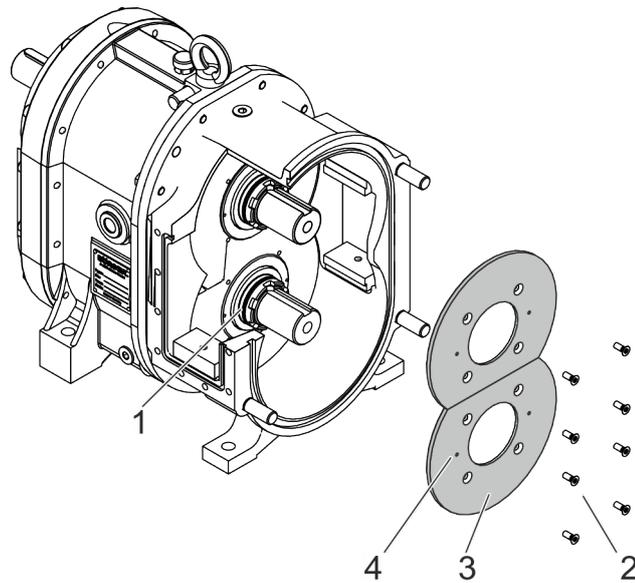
Par ex. Plaque d'usure axiale, en deux parties
